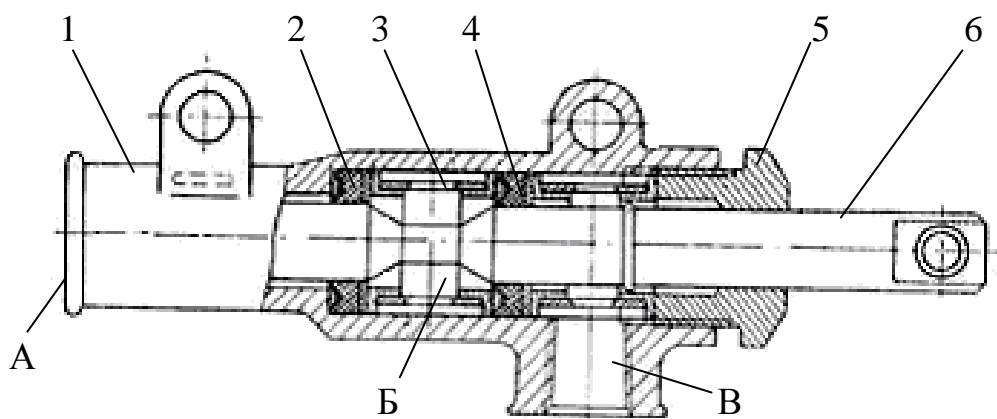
Конструкция крана управления стояночным тормозом прицепа грузовых автомобилей УРАЛ: 1 – корпус; 2 и 4 – уплотнительные манжеты; 3 – втулка; 5 – направляющая золотника; 6 – золотник; А – вывод из воздушного баллона; Б – вывод к клапану управления тормозами прицепа; В – вывод в атмосферу
